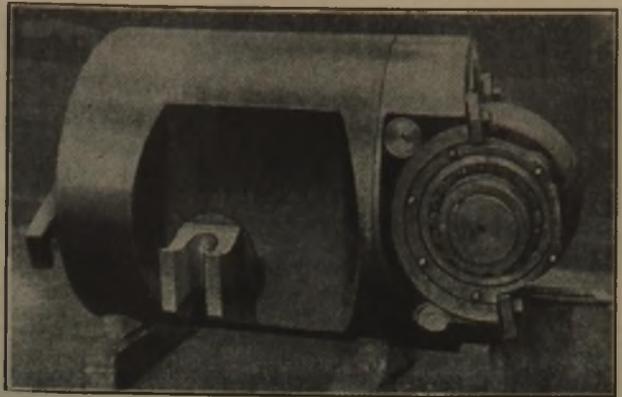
Trommel zum Schrägwalzwerk mit eingebauter Schrägwalze.
